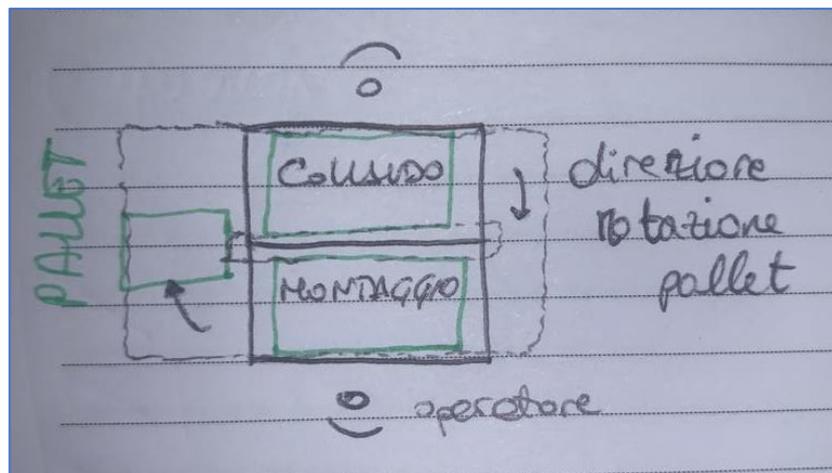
Layout ipotizzato per il banco unico di montaggio
